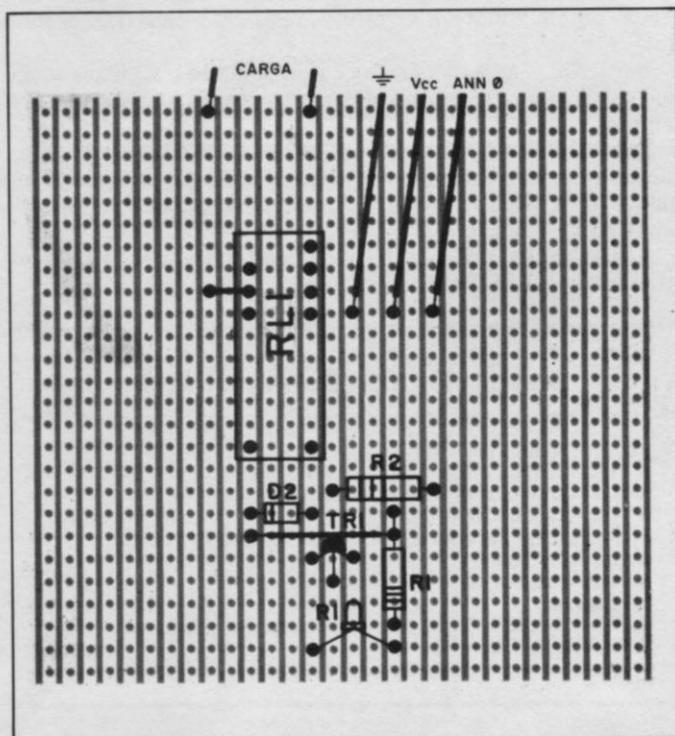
Placa de circuito impresso universal 12,5 x 7,5, vista pela face dos componentes.
